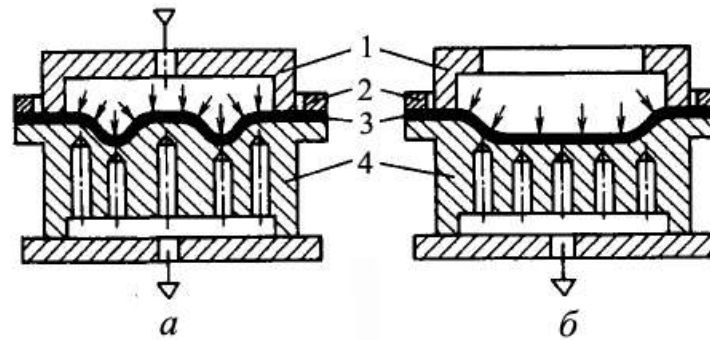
Схема пневматичного (а) і вакуумного (б) формування ПКМ
